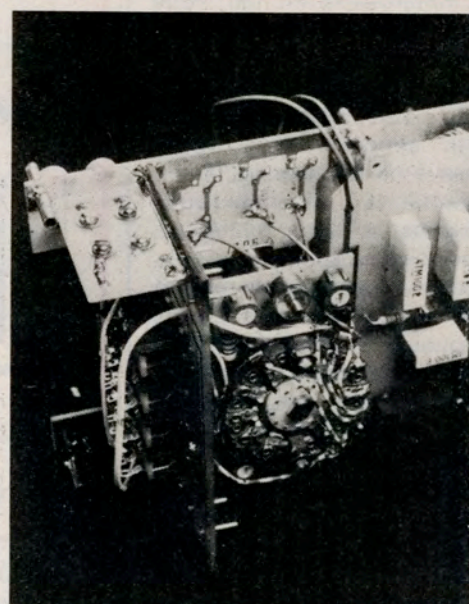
Photo K. - Gros plan sur la plaquette à fusibles E. Noter la soudure dans l'angle supérieur E/B.
